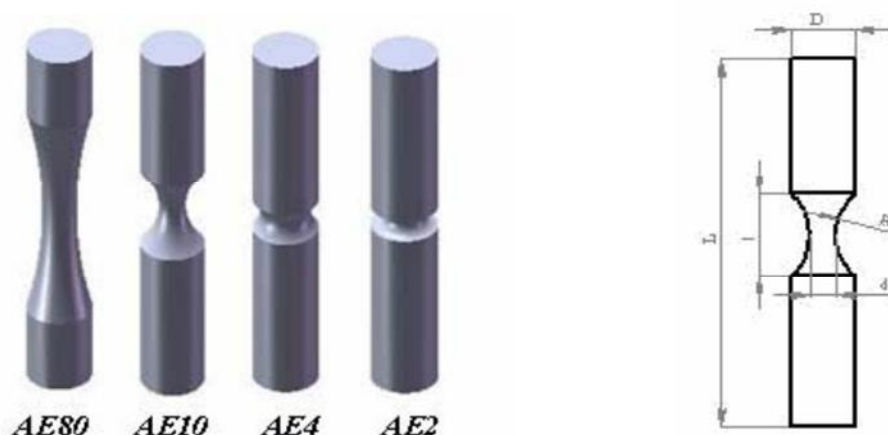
Géométrie des éprouvettes sabliers. [23]
